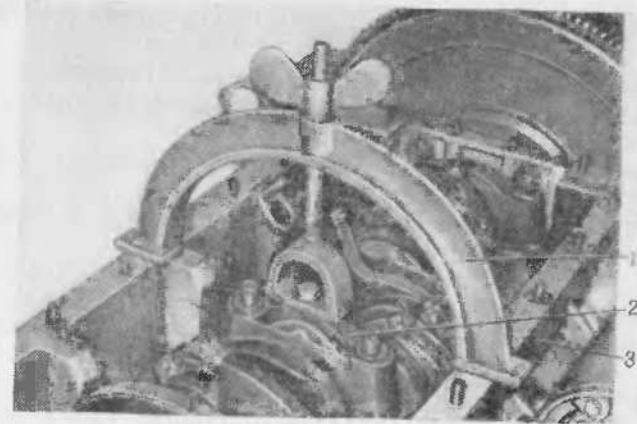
Спрессовка крышек коренных подшипников коленчатого вала двигателя:
